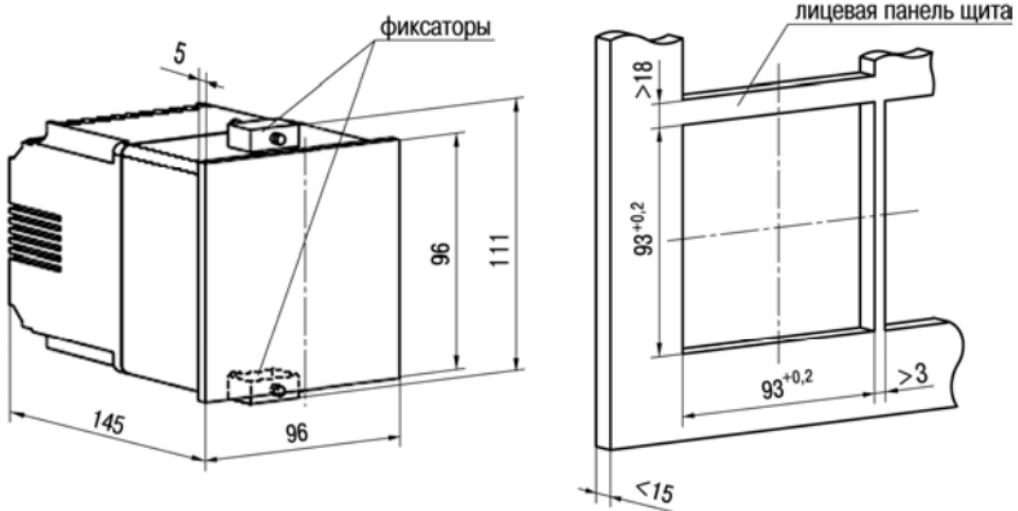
Габаритный чертеж прибора в корпусе Щ4
